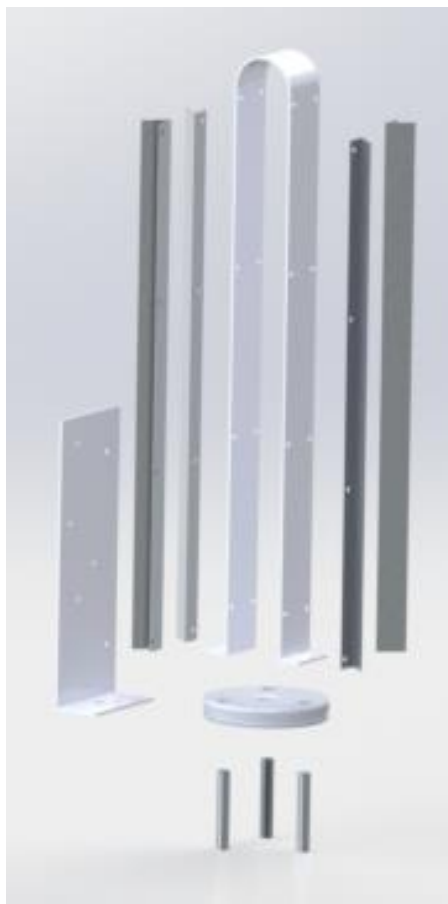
Explosionado soporte (Fuente: propia) Figura 5.16. Ensamblaje soporte (Fuente: propia)
